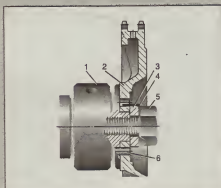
"Штатная" конструкция соединения распределительного вала и звездочки: 1 – распределительный вал; 2 – звездочка; 3 – опорная шайба; 4 – контрольная (фиксирующая) шайба; 5 – центральный болт; 6 – штифт.
